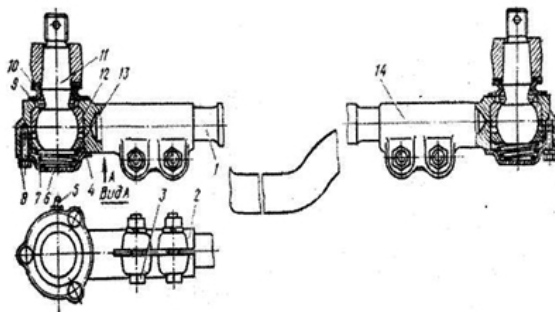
Поперечная рулевая тяга: 1-поперечная тяга; 2,14 - наконечники; 3,8 -болты; 4 -уплотнительная прокладка; 5 -масленка; 6 - крышка; 7 - пружина; 9 - защитная накладка; 10 -обойма накладки; 12,13 - вкладыши.
